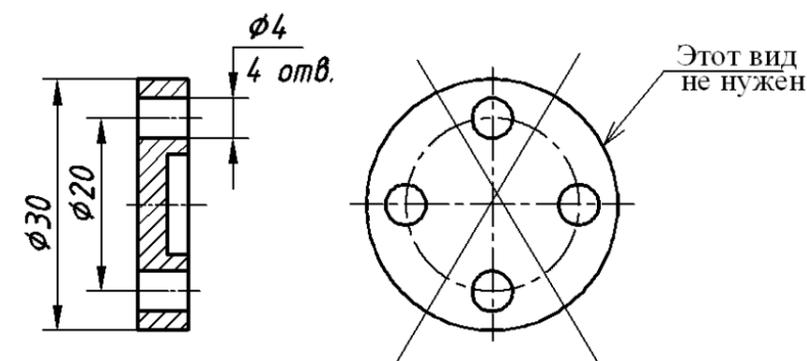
Изображение круглой детали с одинаковыми и равномерно расположенными отверстиями
